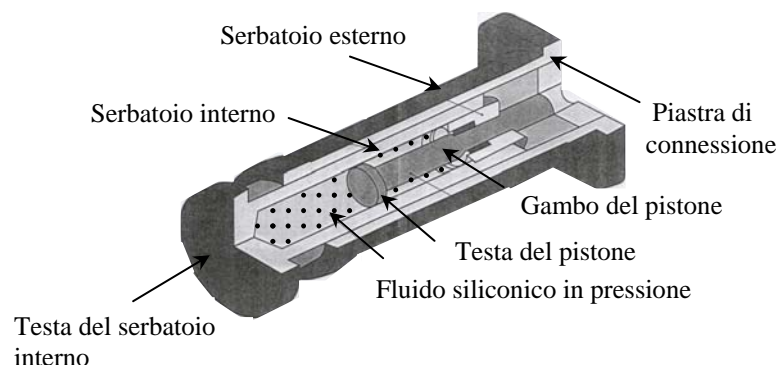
Schema di sezione longitudinale di un dispositivo siliconico.
